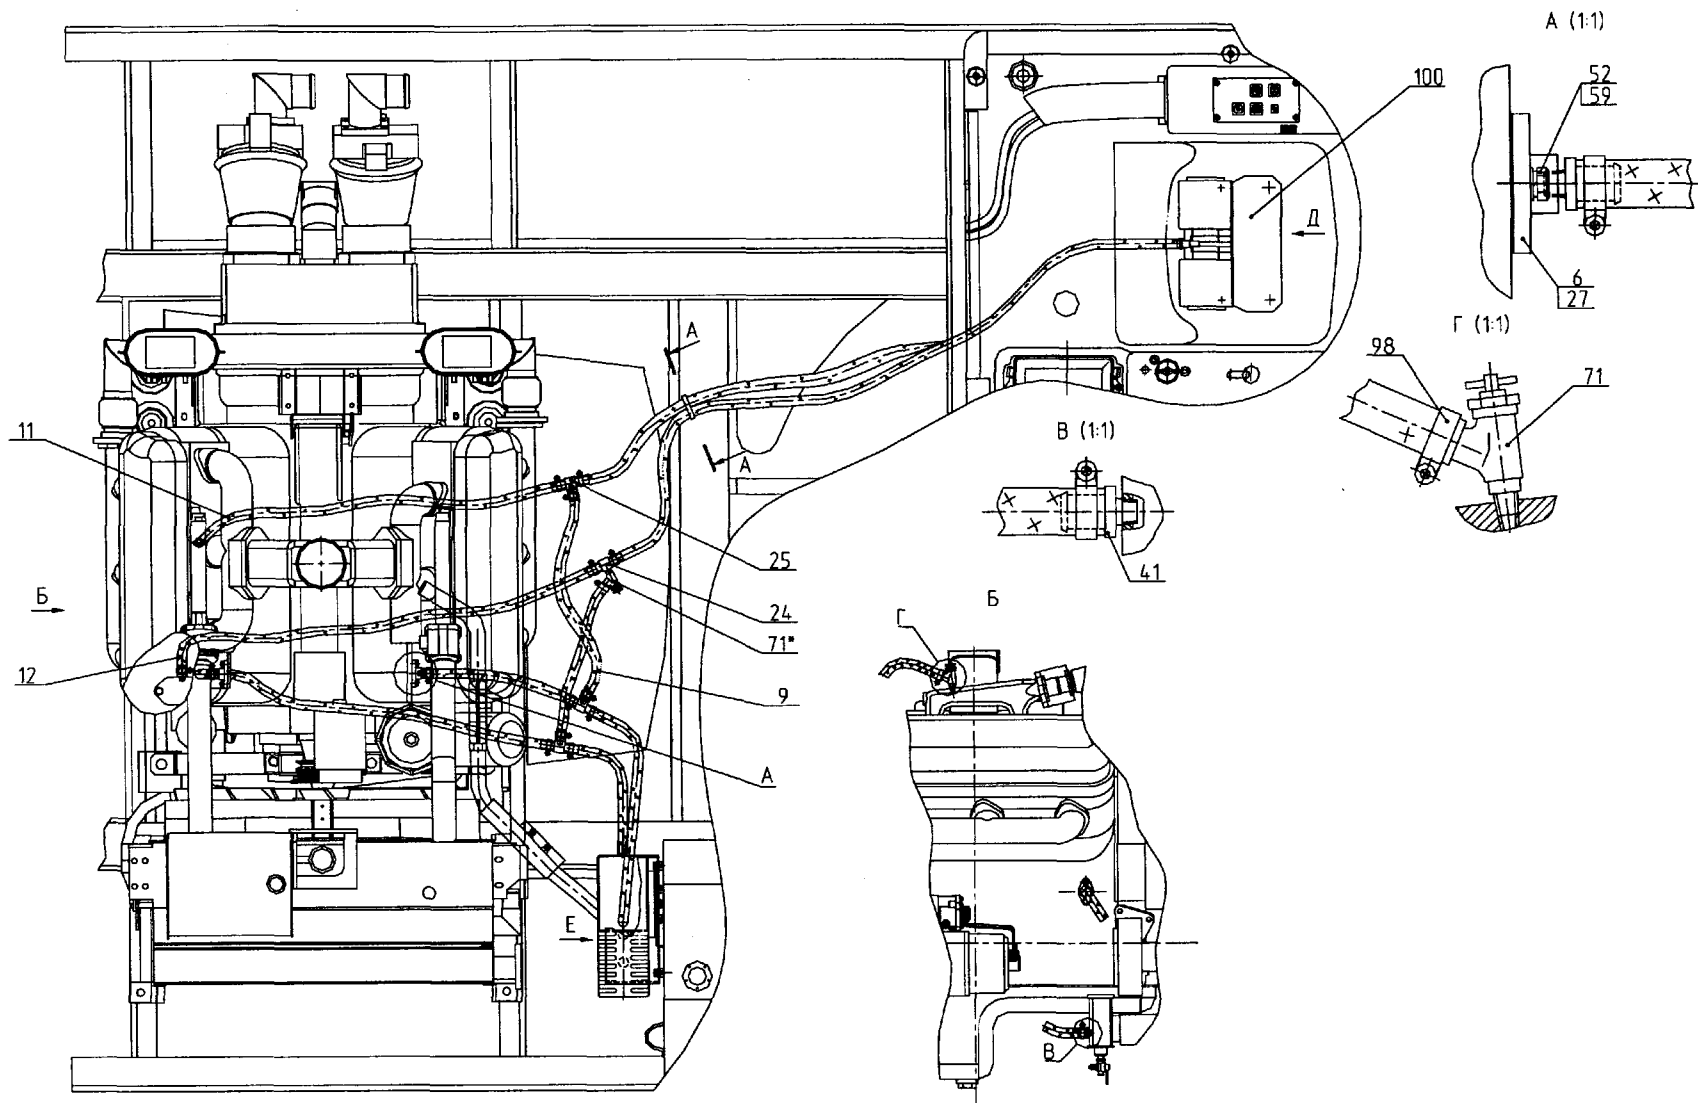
Установка предпускового подогрева двигателя и отопления кабины
